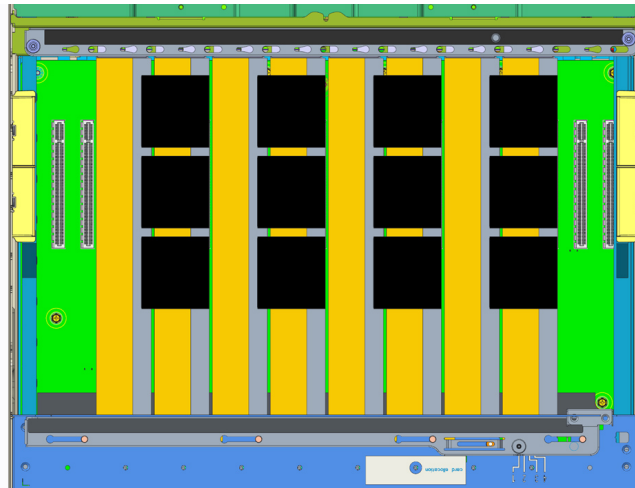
Draufsicht der NVLink-Brücke für die A100-GPU
